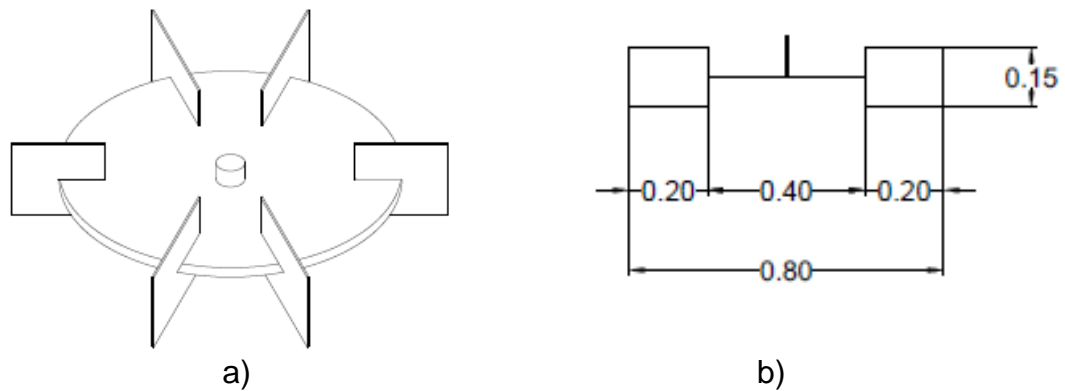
Diseño del impulsor de mezclador de reactor #4; a) vista superior, b) vista frontal
